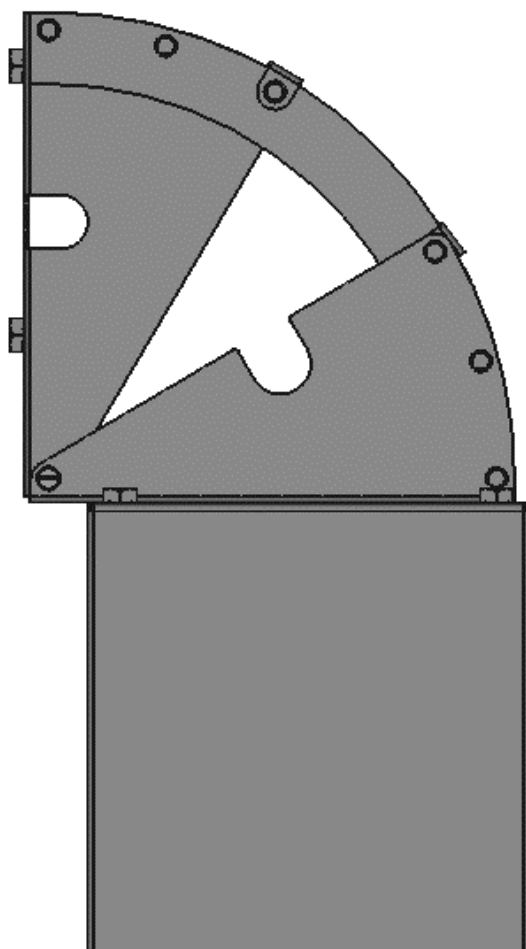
Внешний вид козырька с кронштейном вид сверху
